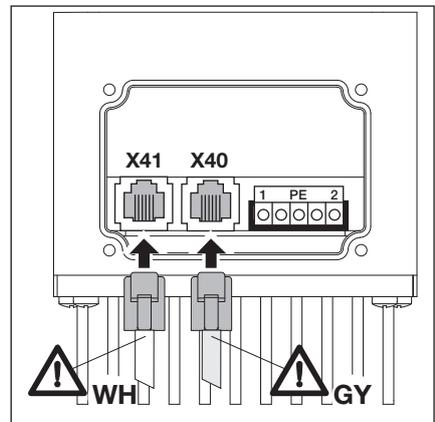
Anschluss der Systemleitung an die Motoranschlussplatine. Farben beachten!
